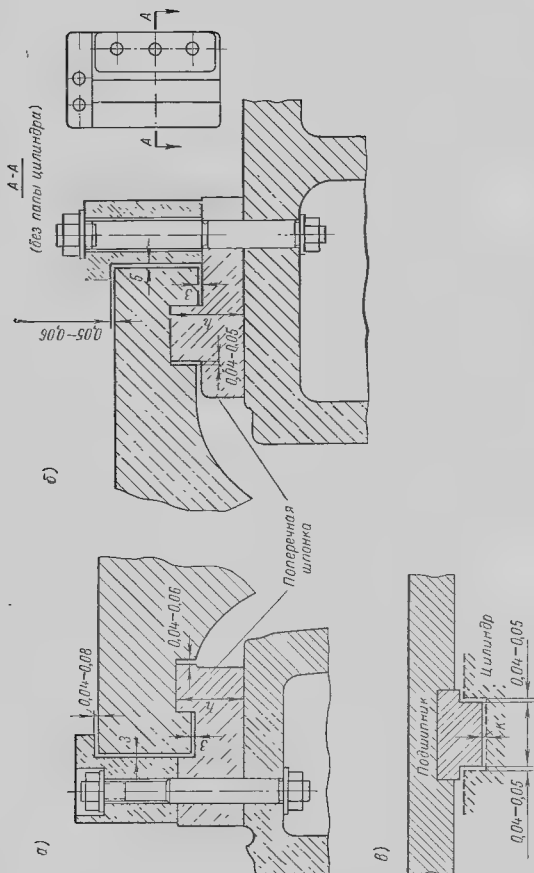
Конструкция соединения цилиндра с корпусом подшипника; α — поперечная шпонка у переднего подшипника; β — то же у среднего; ϑ — вертикальная шпонка
